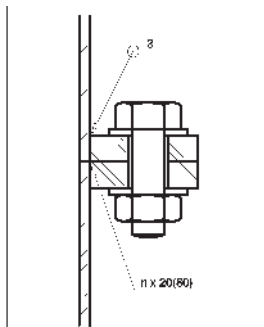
Flanschverbindung mit Flansche, geschweißt.
